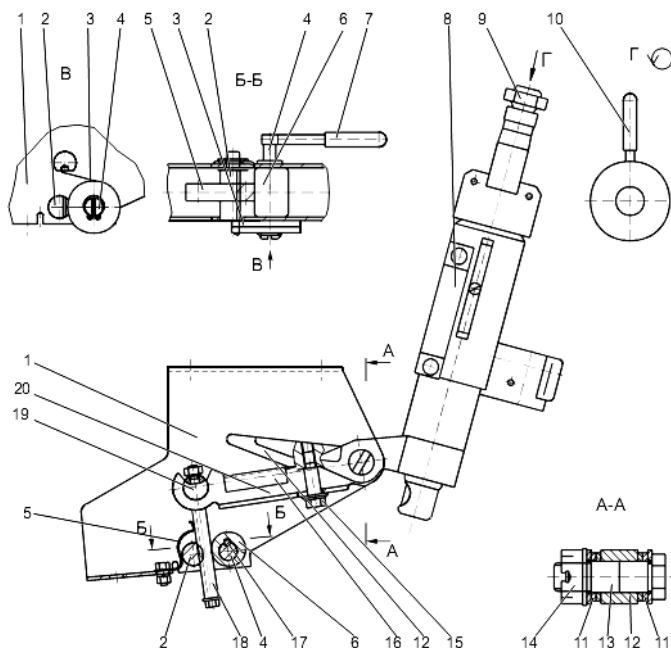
Регулируемая рулевая колонка с травмобезопасным устройством:
